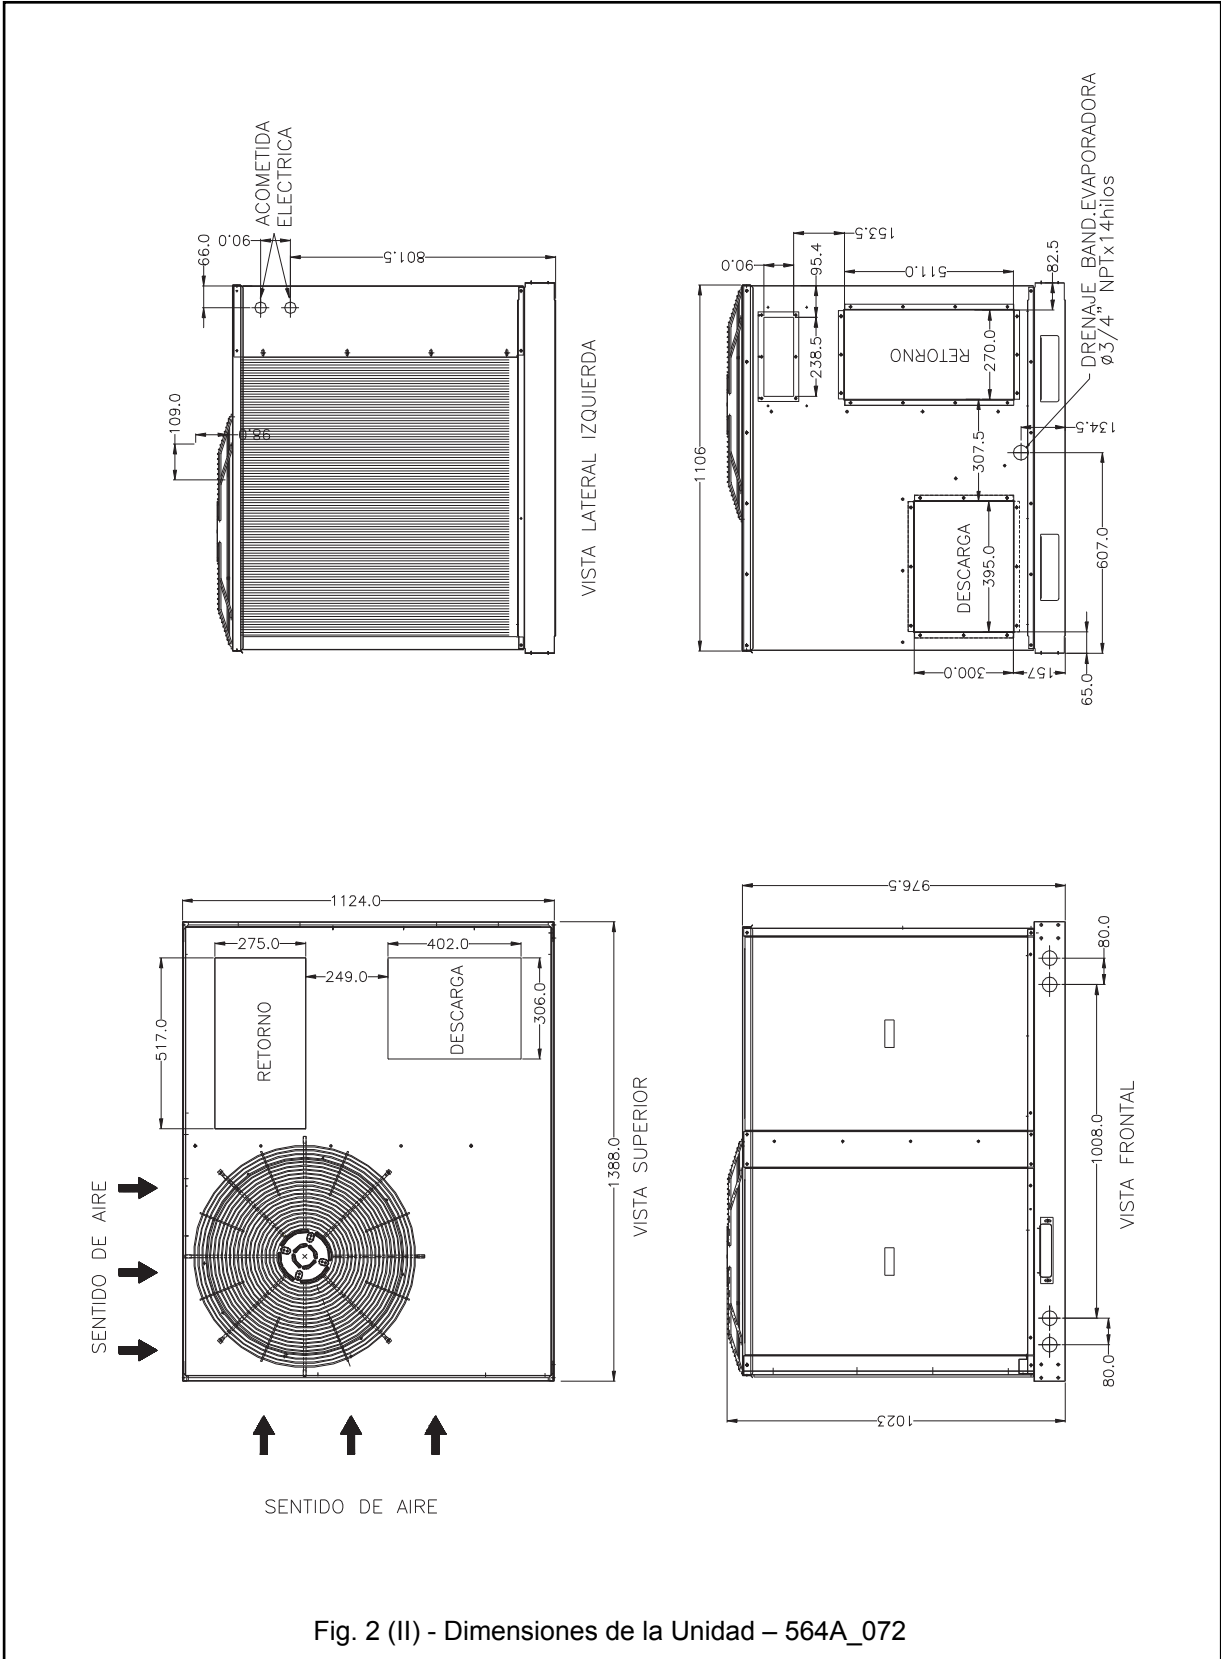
(II) - Dimensiones de la Unidad – 564A_072
